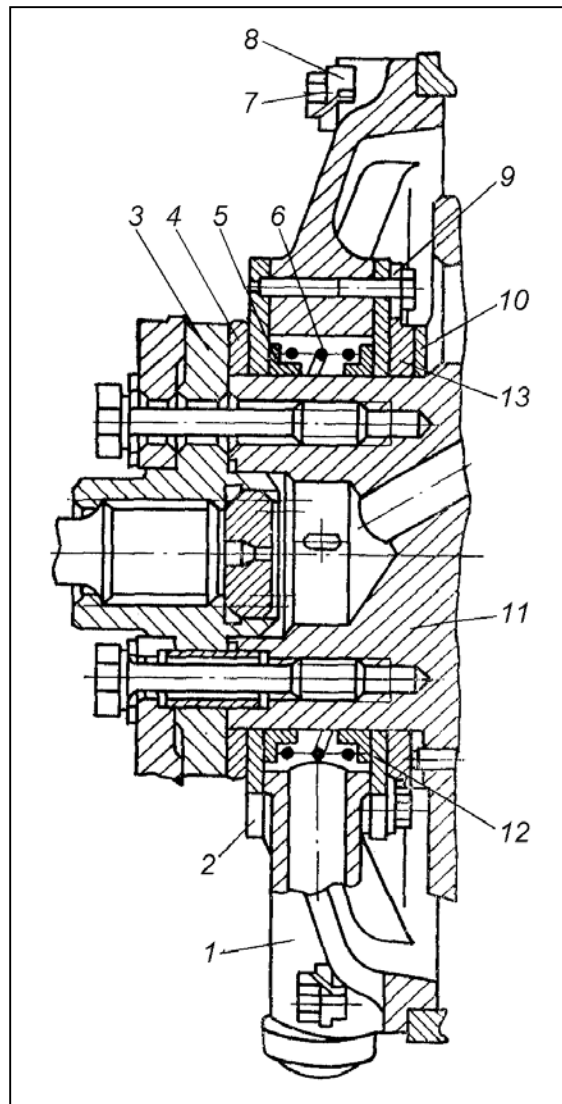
Упорный подшипник ЯМЗ-240Б:
